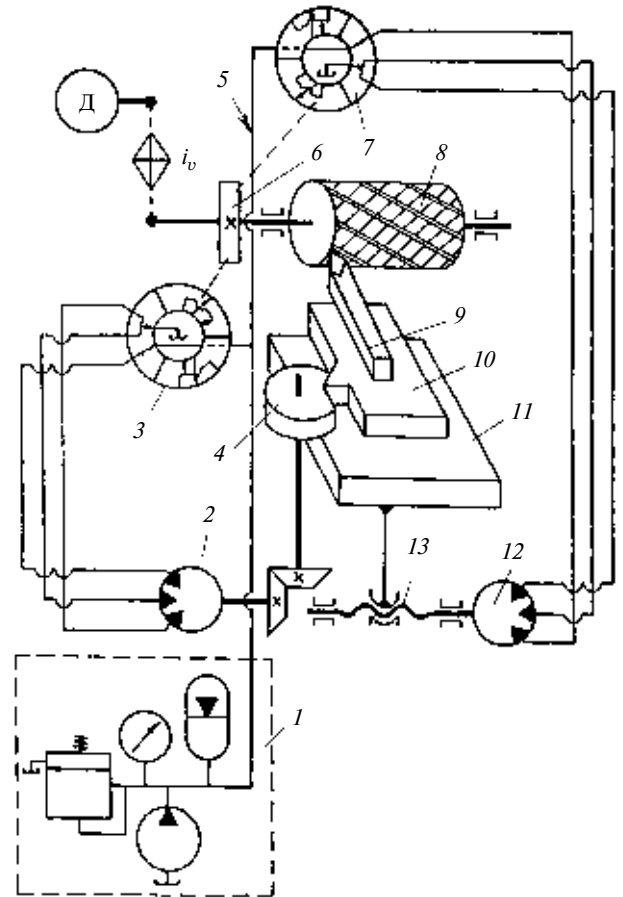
Структурная схема токарно-затыловочного станка с гидравлической внутренней связью для затылования гребенчатых фрез:
